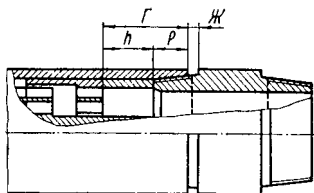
К проверке зажатия системы корпуса (определение высоты регулировочного кольца 15, рис. 7).
